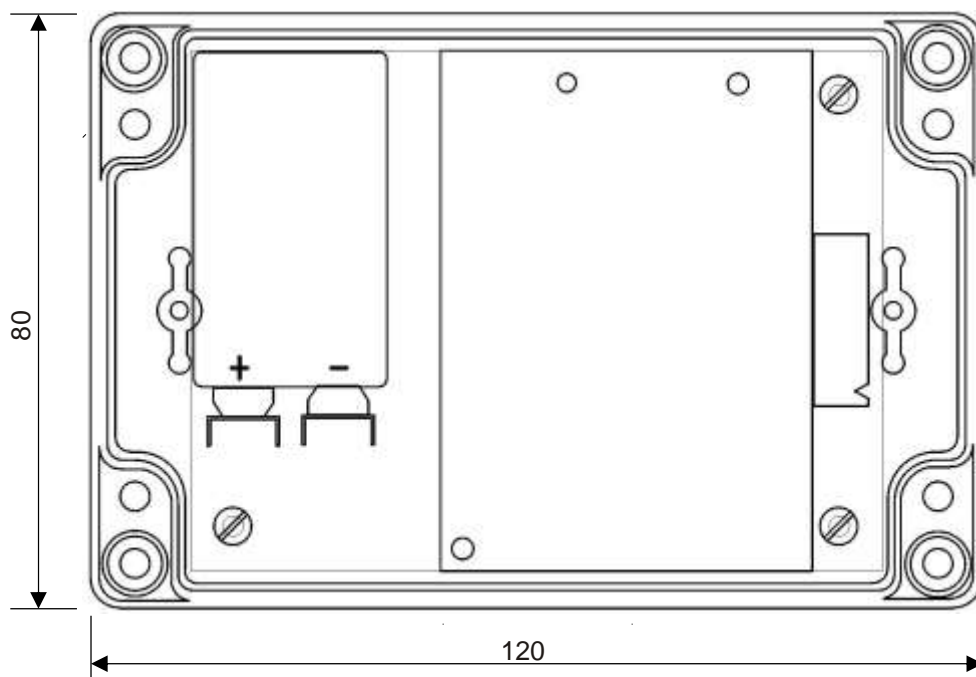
Чертеж радиомодуля VX-RGW с размерами (без крышки)
